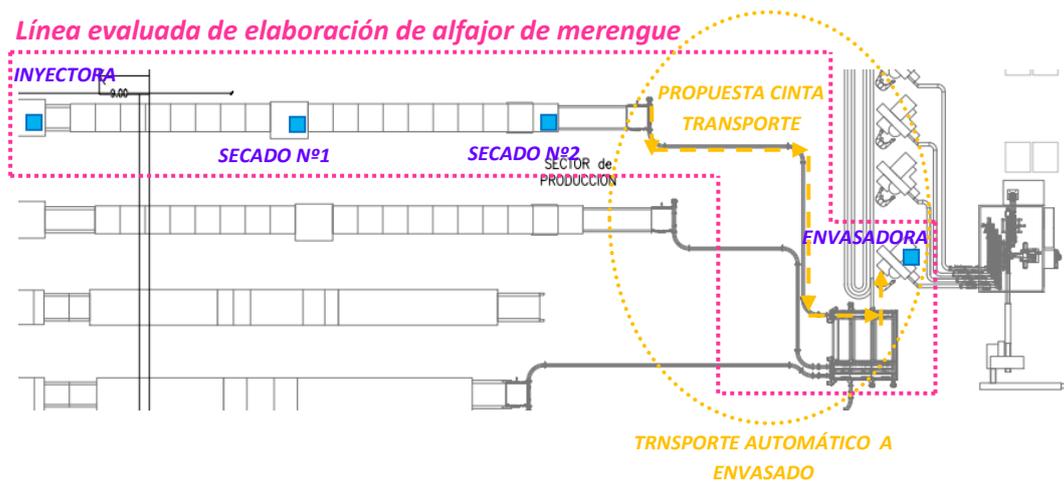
Plano modificaciones al final de las línea para transporte automático de alfajores a envasado
